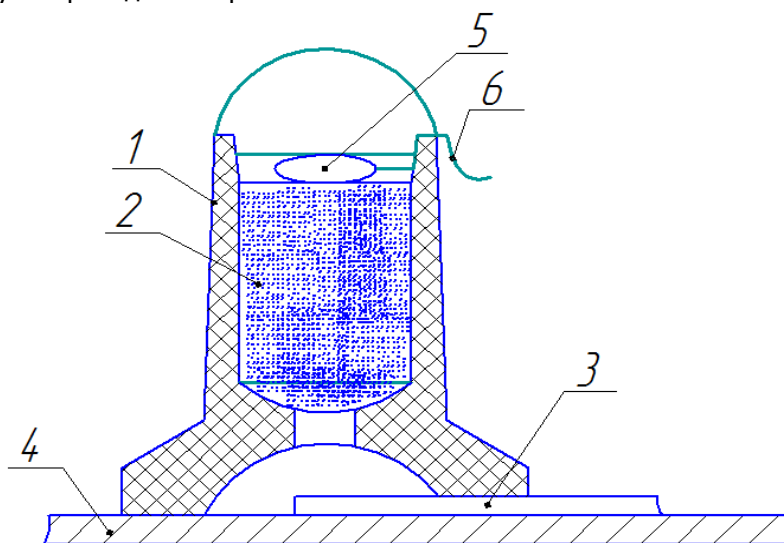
Реализуемая схема термитной сварки вывода ЭХЗ
